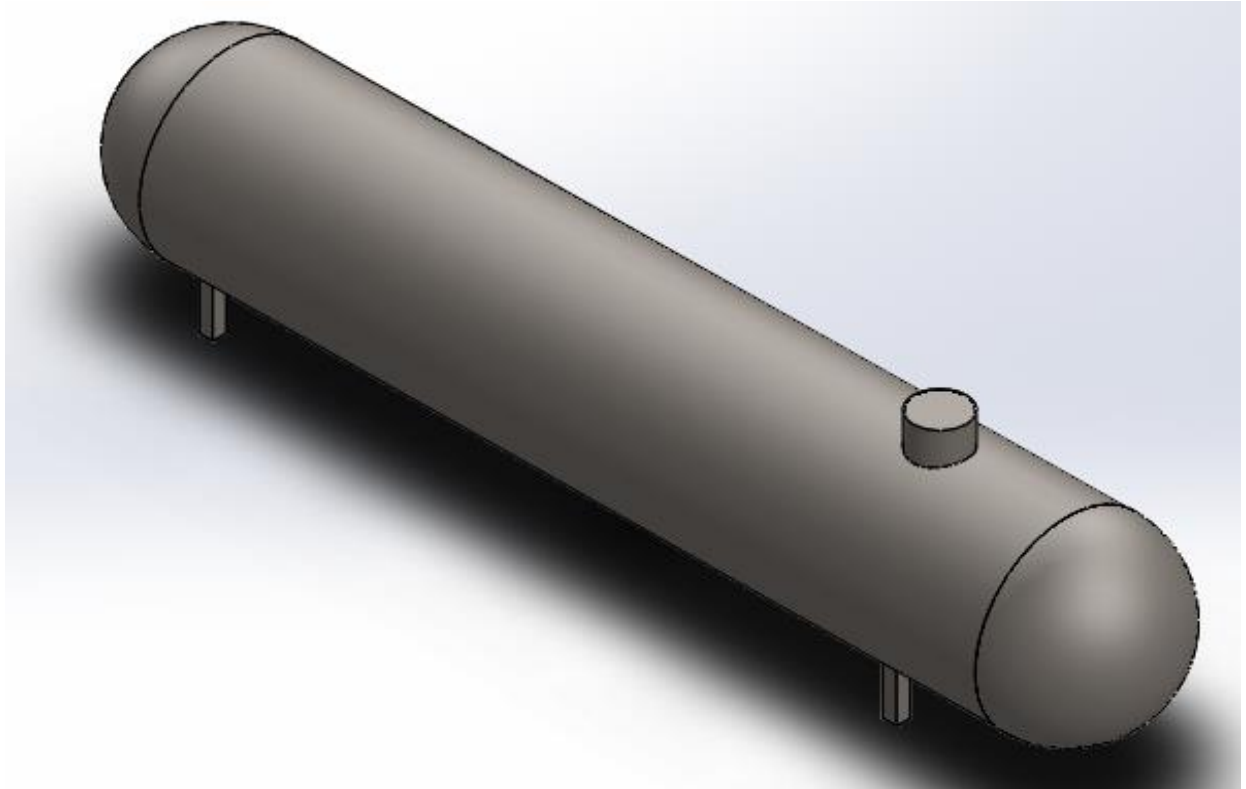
Загальний вигляд зварного горизонтального резервуару
